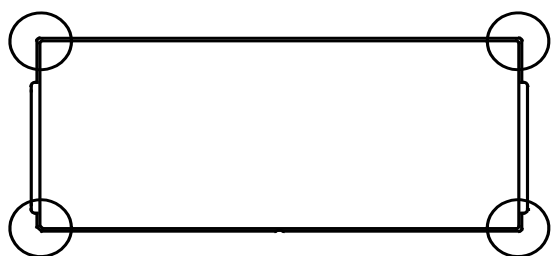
Vue d'en haut d'un support montrant les emplacements de mesure pour les dimensions d'encombrement
